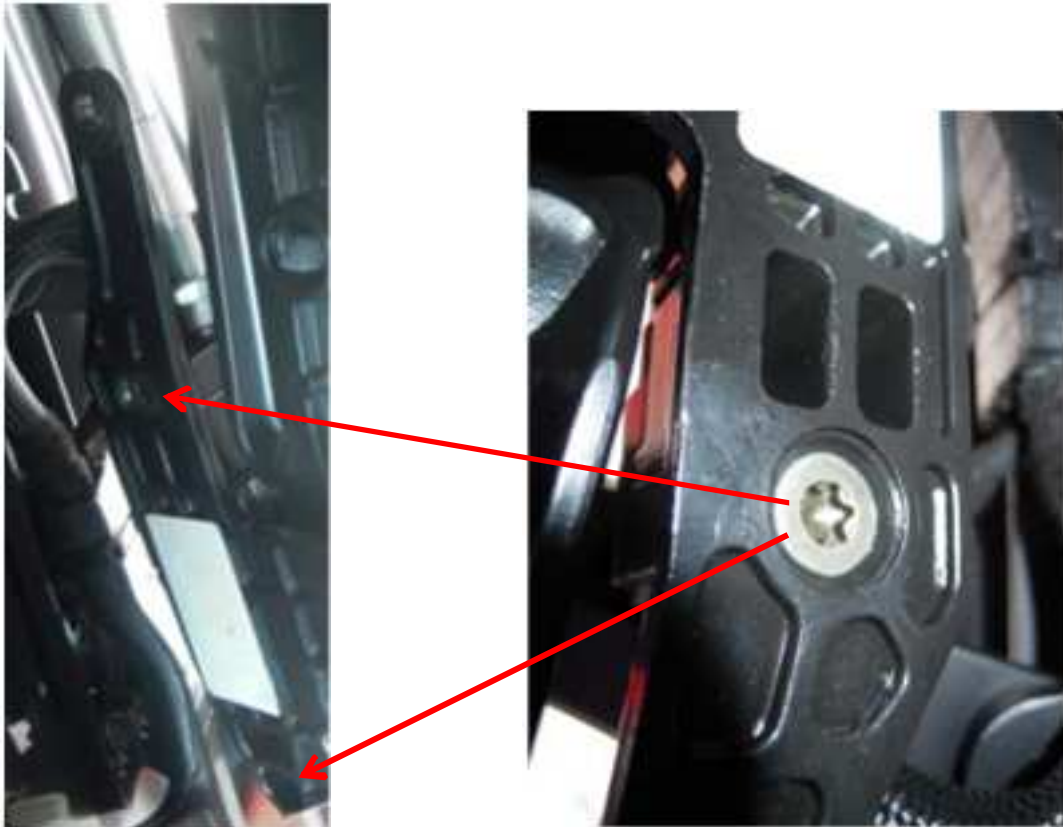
2 Tx30-Schrauben zur Befestigung der Lagerplatte
